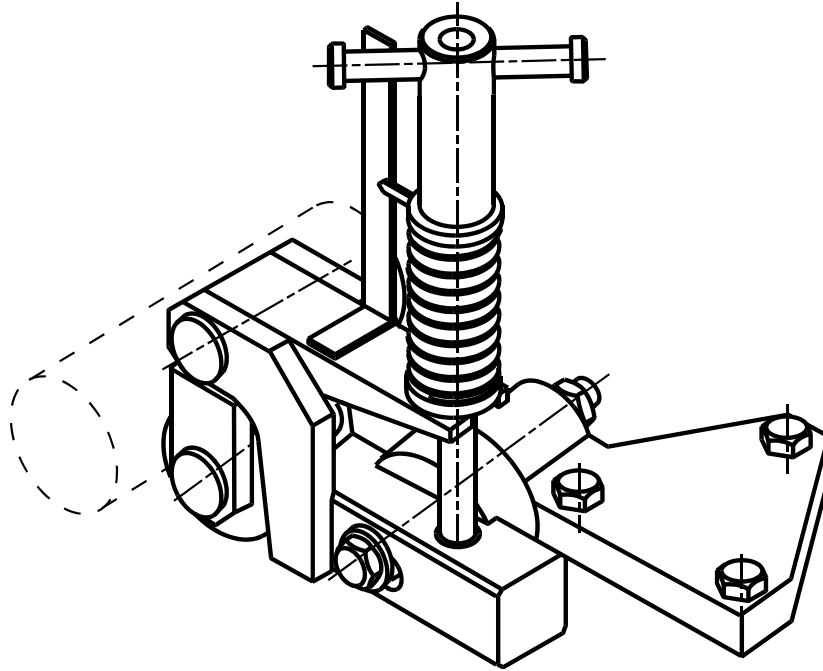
Загальний вигляд одно роликового пристрою для зміцнення поверхні деталі.
